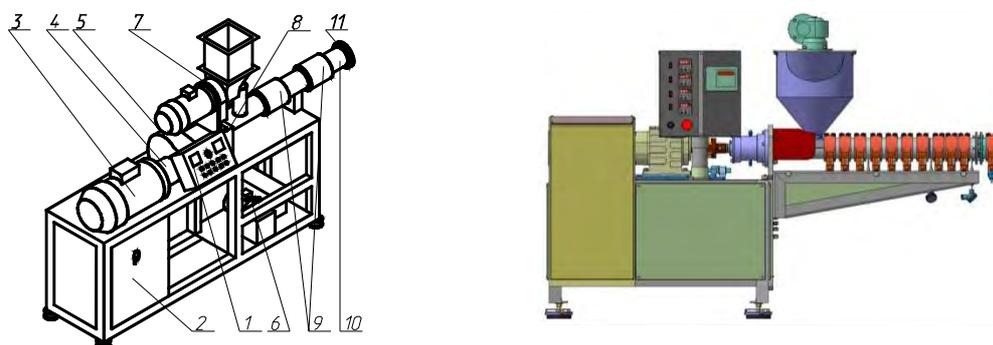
Экструдер с включенными в конструкции термодатчиками: 1 – Пульт управления; 2 – Шкаф управления; 3 – Электродвигатель привода шнека; 4 – Муфта соединительная; 5 – Редуктор; 6, 7 – Дозатор компонентов RDF; 8 – Опорный узел; 9 – Нагреватели; 11 – Термодатчик; 11 – Матрица формообразующая;
